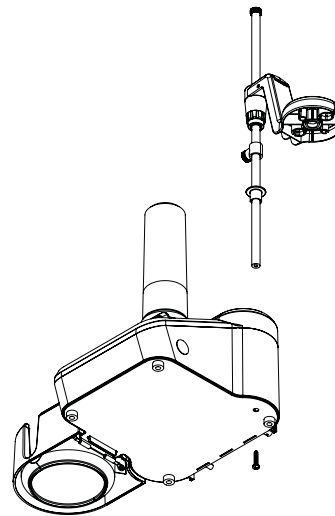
Position der Befestigungsschraube zum Festziehen des Elektrodenhalterschafts
